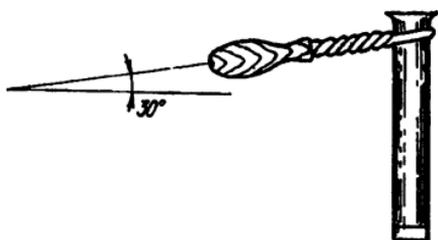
Приспособление к зубилу для смягчения реакции на удар
